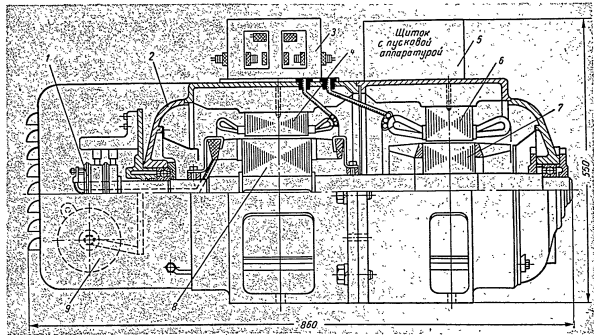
Преобразователь частоты типа ПСЧ-5: 1 — узел контактных колец; 2 — подшипниковый щит; 3 — стабилизирующий трансформатор; 4 — статор генератора; 5 — щиток с пусковой аппаратурой; 6 — статор электродвигателя; 7 — ротор электродвигателя; 8 — ротор генератора; 9 — селеновый выпрямитель.
